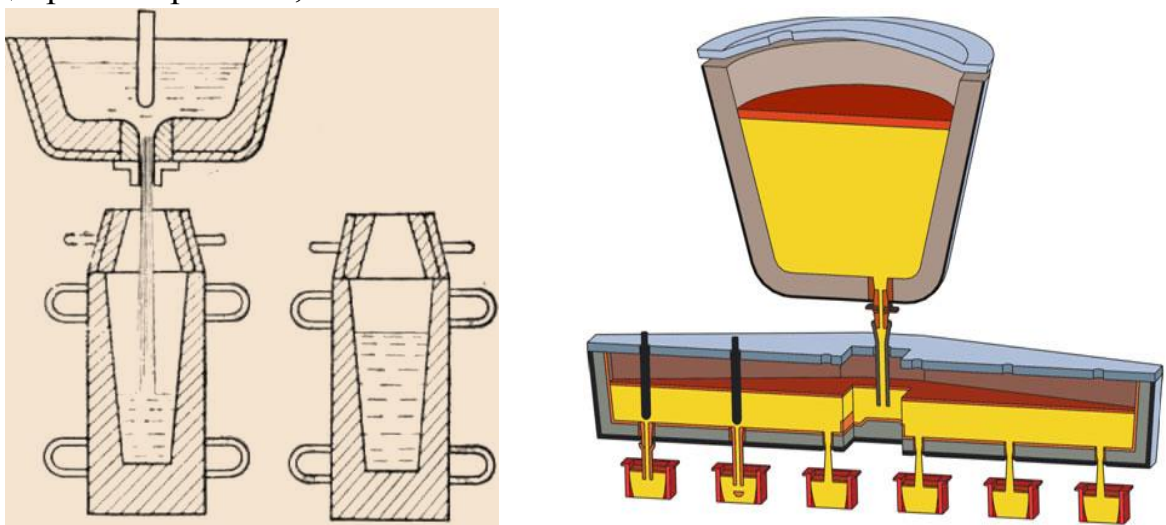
Схема разливки стали сверху непосредственно из ковша
